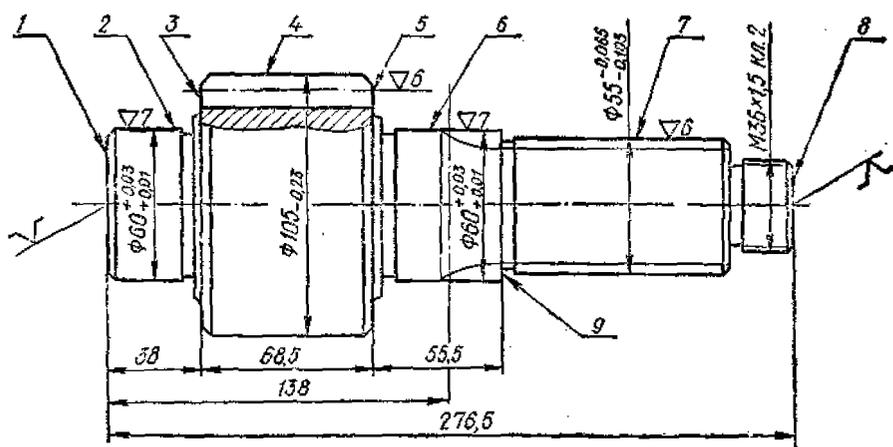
Шестерня ведущая (чертеж и схема установки при обработке поверхностей $\varnothing 60 \pm 0.03$)
